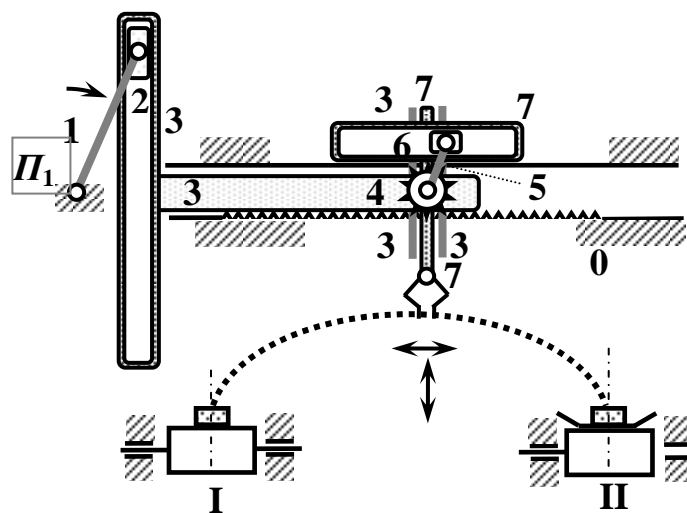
Манипулятор укладчика (0—стойка, зубчатая рейка: 1—кривошип; 2—камень; 3—кулиса, ползун; 4—зубчатое колесо; 5—водило, 6—камень; 7— кулиса, ползушка, схват)
